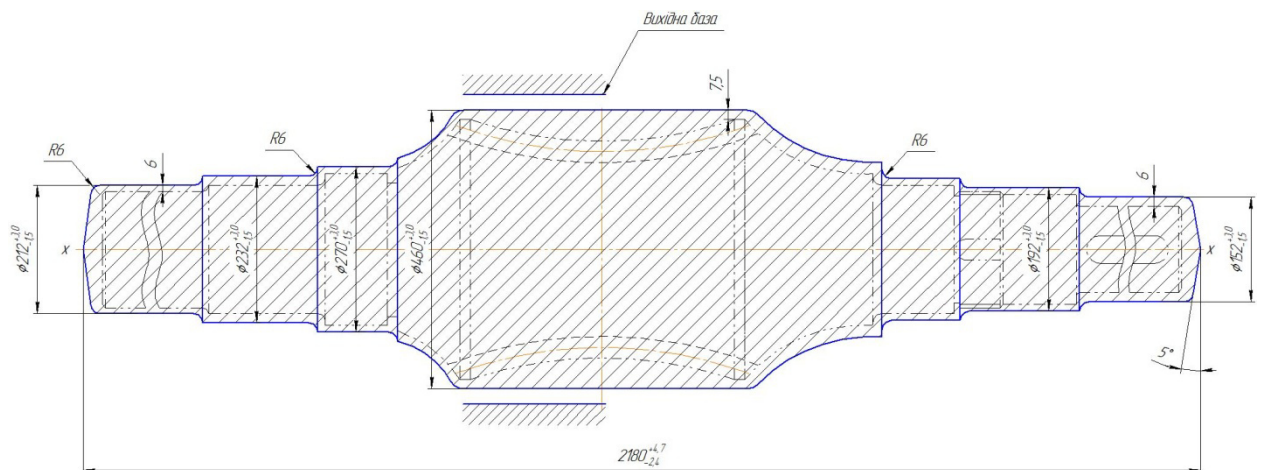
Заготовка деталі «Глобоїдний черв'як»
